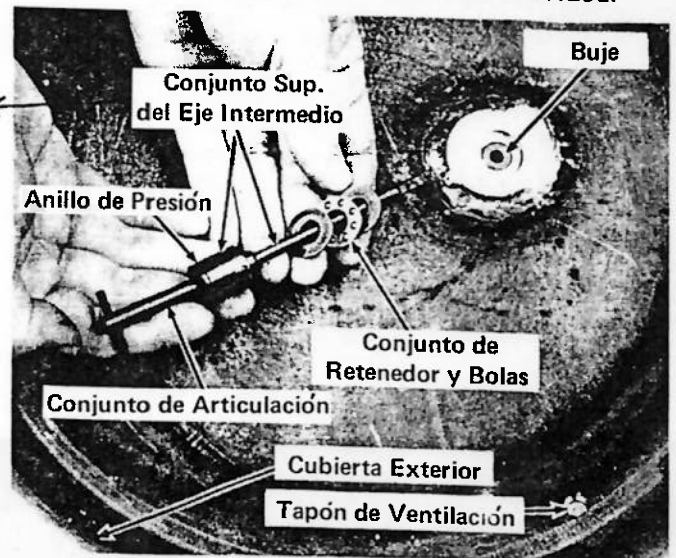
CONJUNTO DEL EJE INTERMEDIO.
